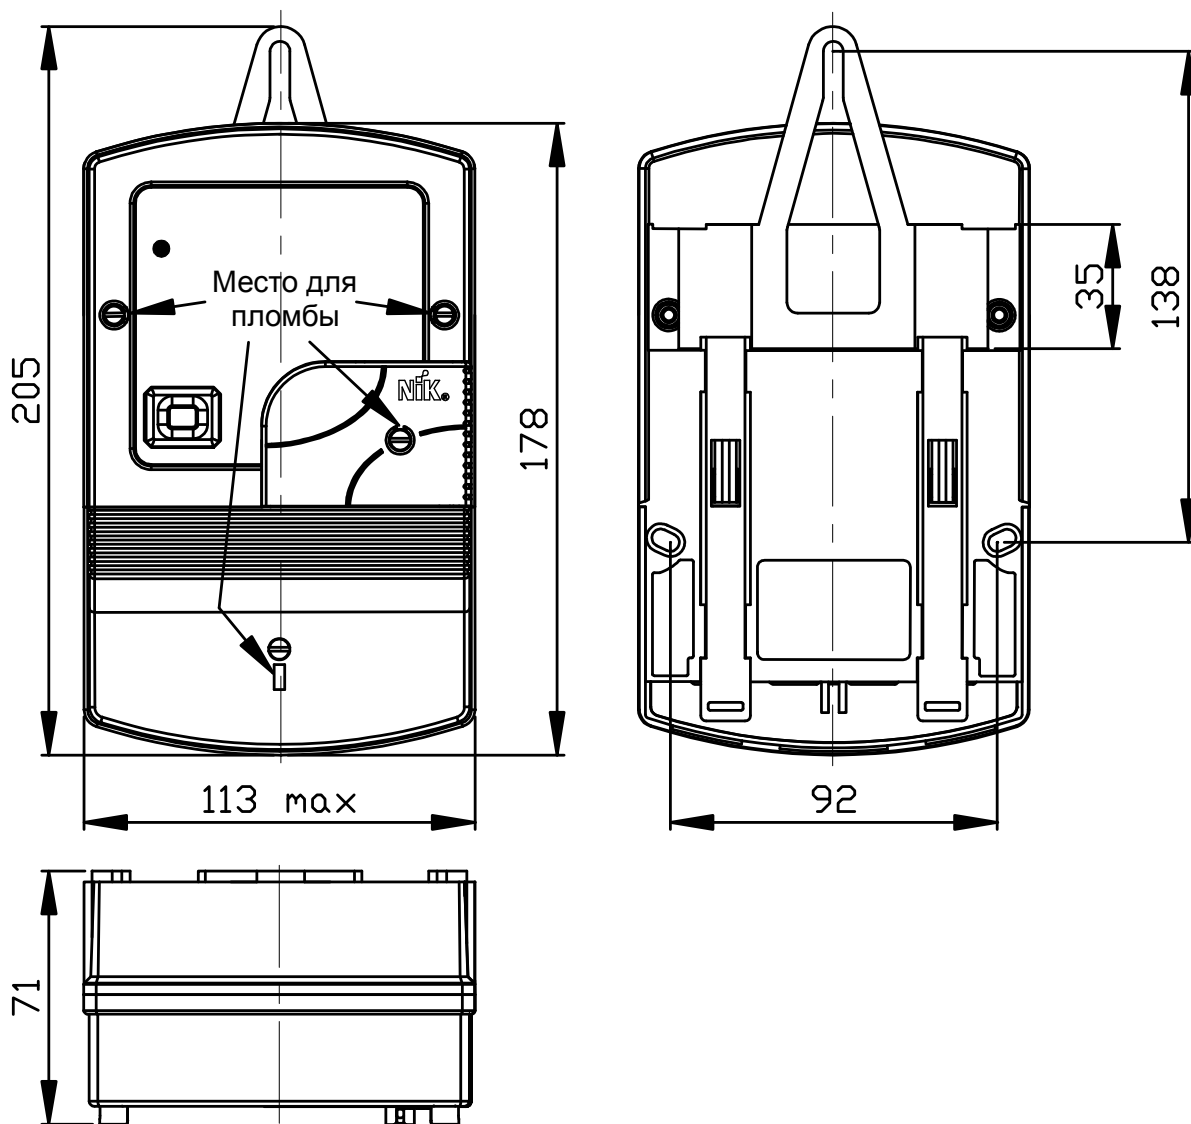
Габаритные и установочные размеры счетчиков
